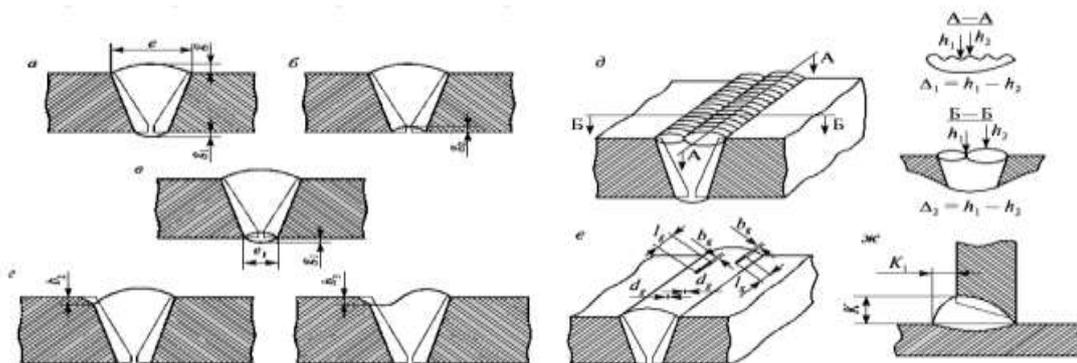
Конструктивные элементы и дефекты сварного шва, подлежащие измерительному контролю
